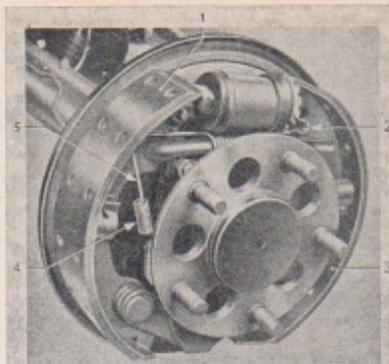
Rückzieher an hinterer Bremsbacke, Bremsanordnung mit gezahnter Einstellmutter am Radbremszylinder, rechte hintere Bremse
